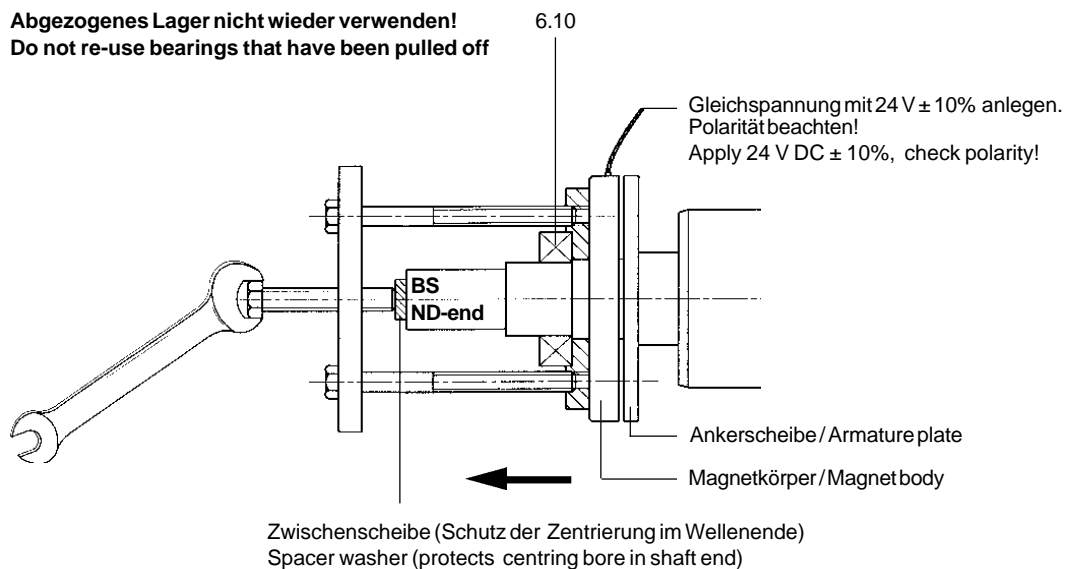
Lagerwechsel bei Motoren mit Bremse / Changing bearings on motors with brake
